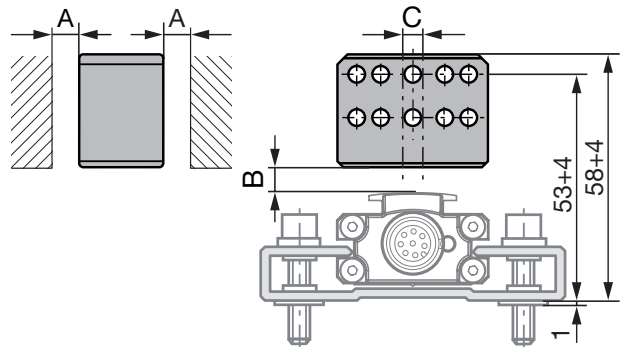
Maße und Abstände mit Positionsgeber BTL6-A-3800-2
